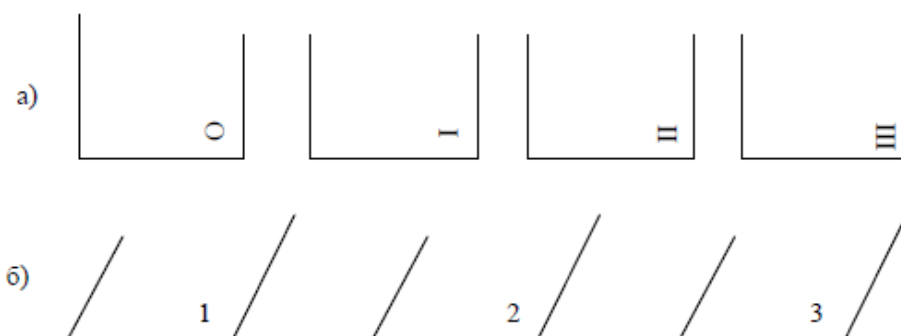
Схема маркировки пиломатериалов и заготовок на пласти:
